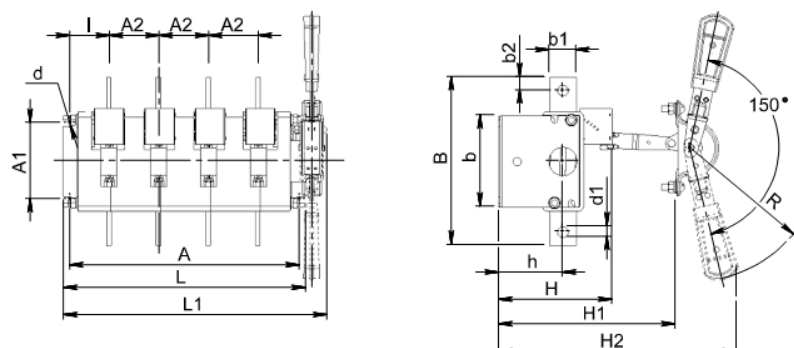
Б Выключатель-разъединитель на одно направление 4-полюсный с передней смещенной рукояткой
